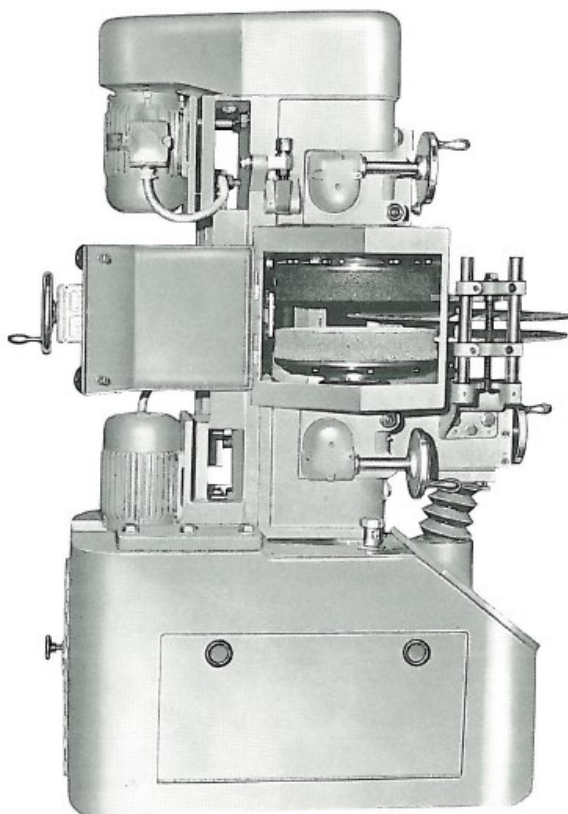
Bruska Bennett CG-350 Crash Grinder [24]
